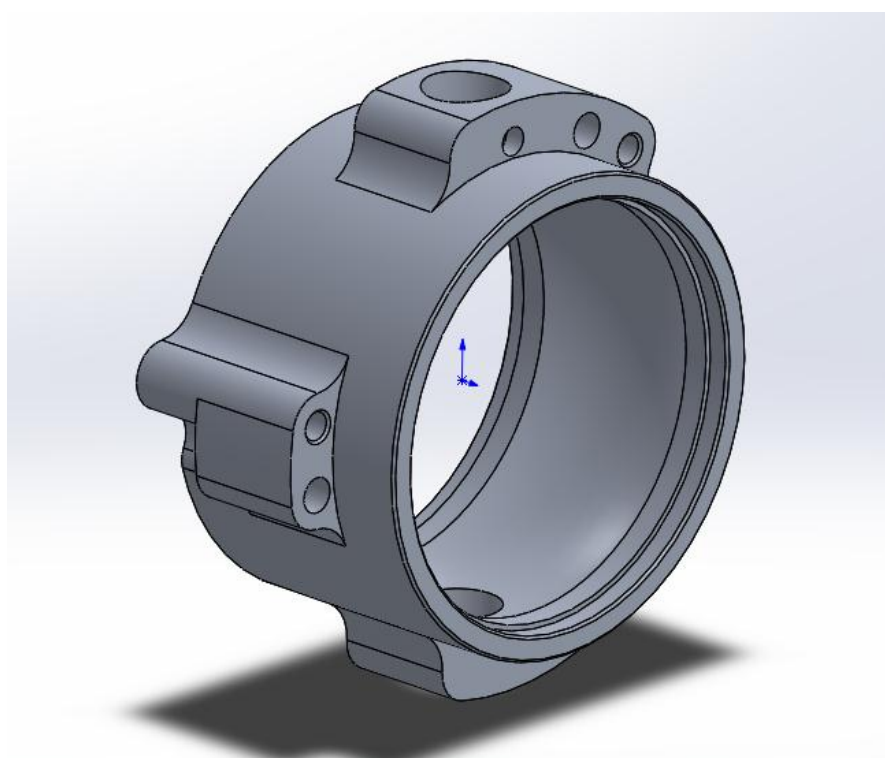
3D модель деталі «Корпус диференціалу»
